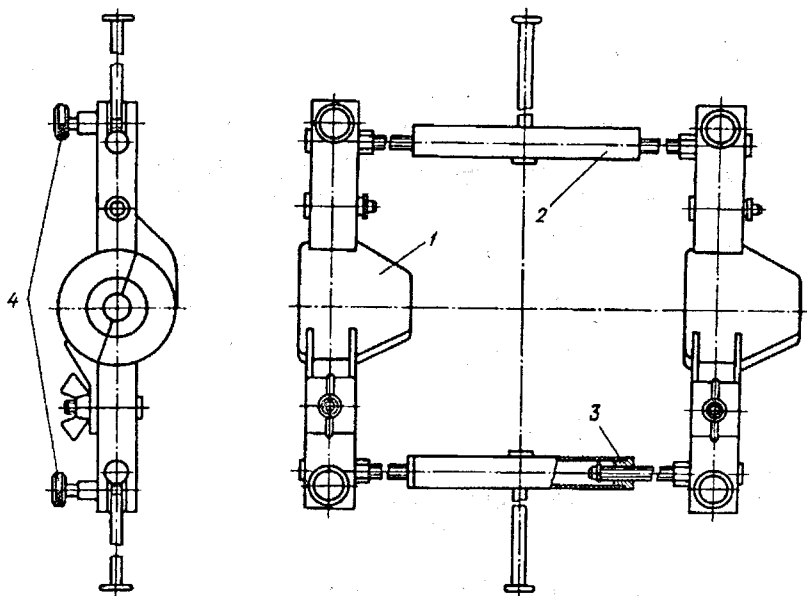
Стяжний гвинтовий полегшений пристрій
